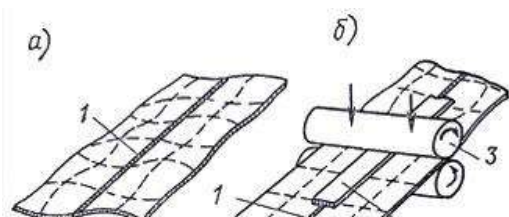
Устранение деформаций в тонколистовых металлических конструкциях а – схема сваренных листов перед прокатыванием, б – схема процесса прокатывания, 1 – схема сварочного шва, 2 – схема накладки, 3 – схема прокатных валков
